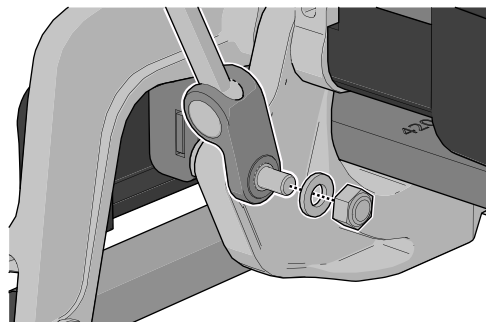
Halten Sie die Gelenkschraube fest, um die Mutter entfernen zu können.
